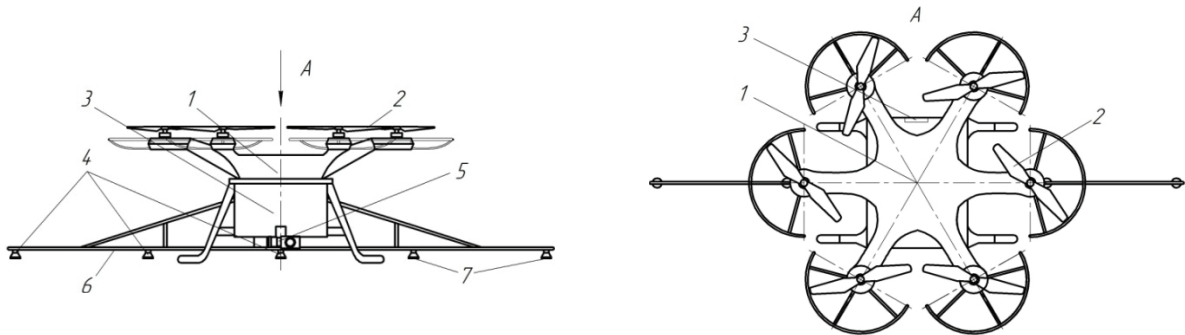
Дрон-обприскувач для хімічної обробки рослин
